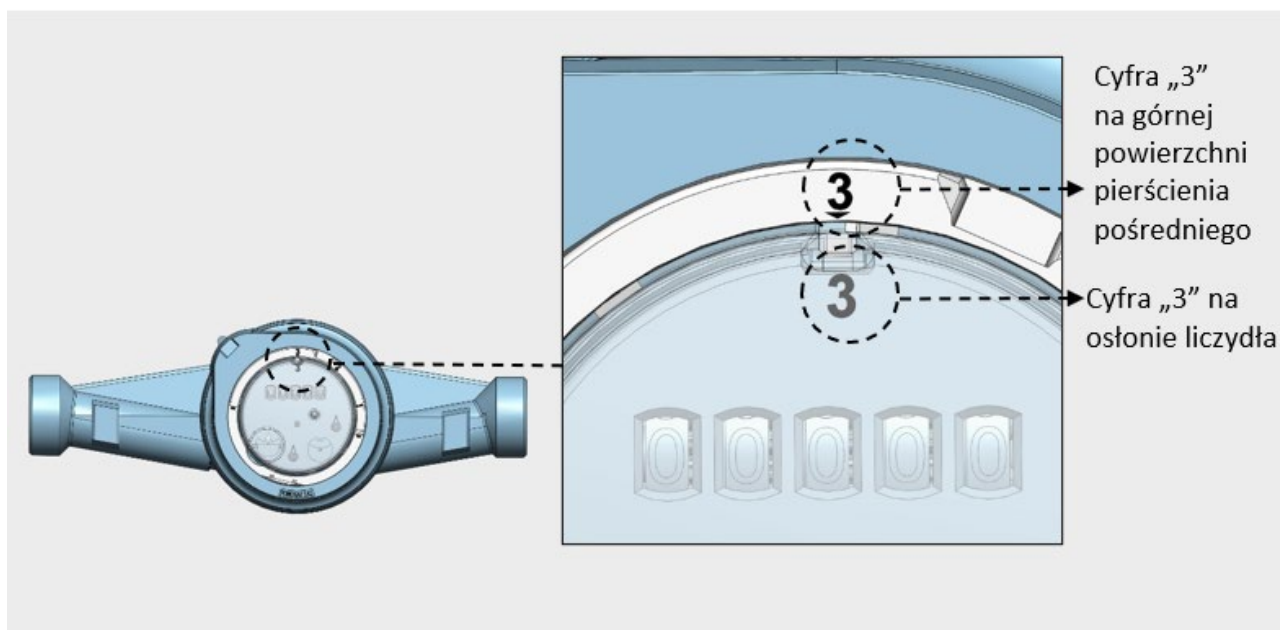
Pozycjonowanie pierścienia blokującego przed montażem na pierścieniu pośrednim.
